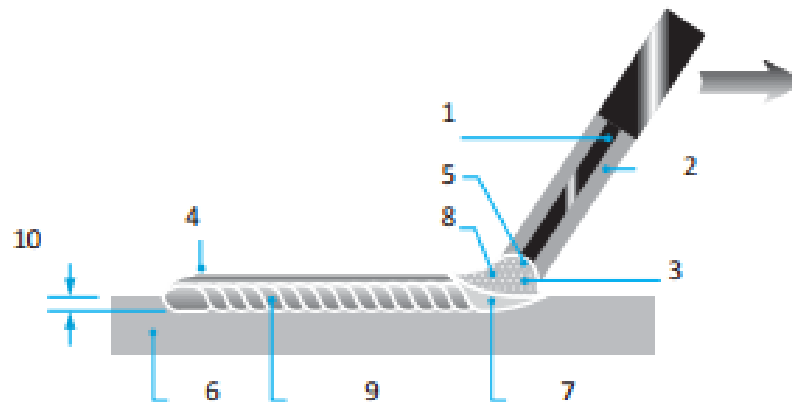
Partes del circuito de soldadura por arco eléctrico
